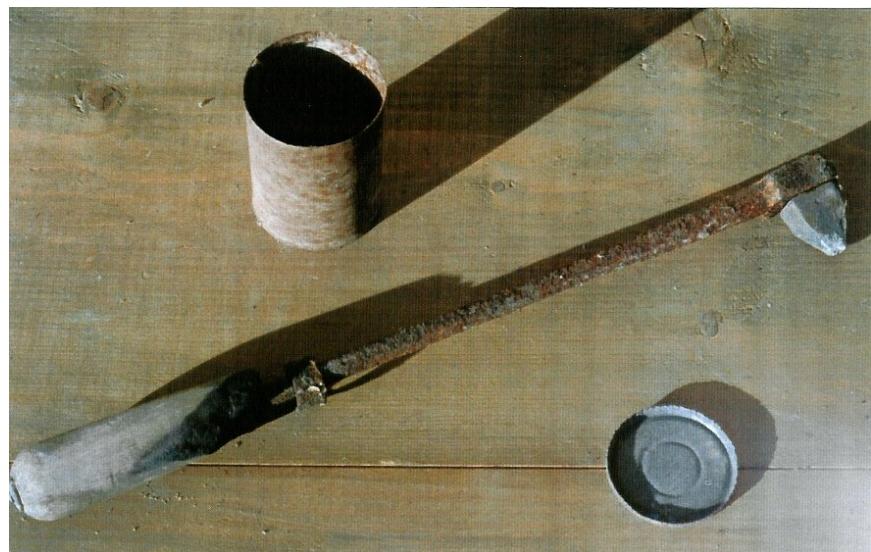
La boîte en fer blanc et son couvercle avec le fer à souder
